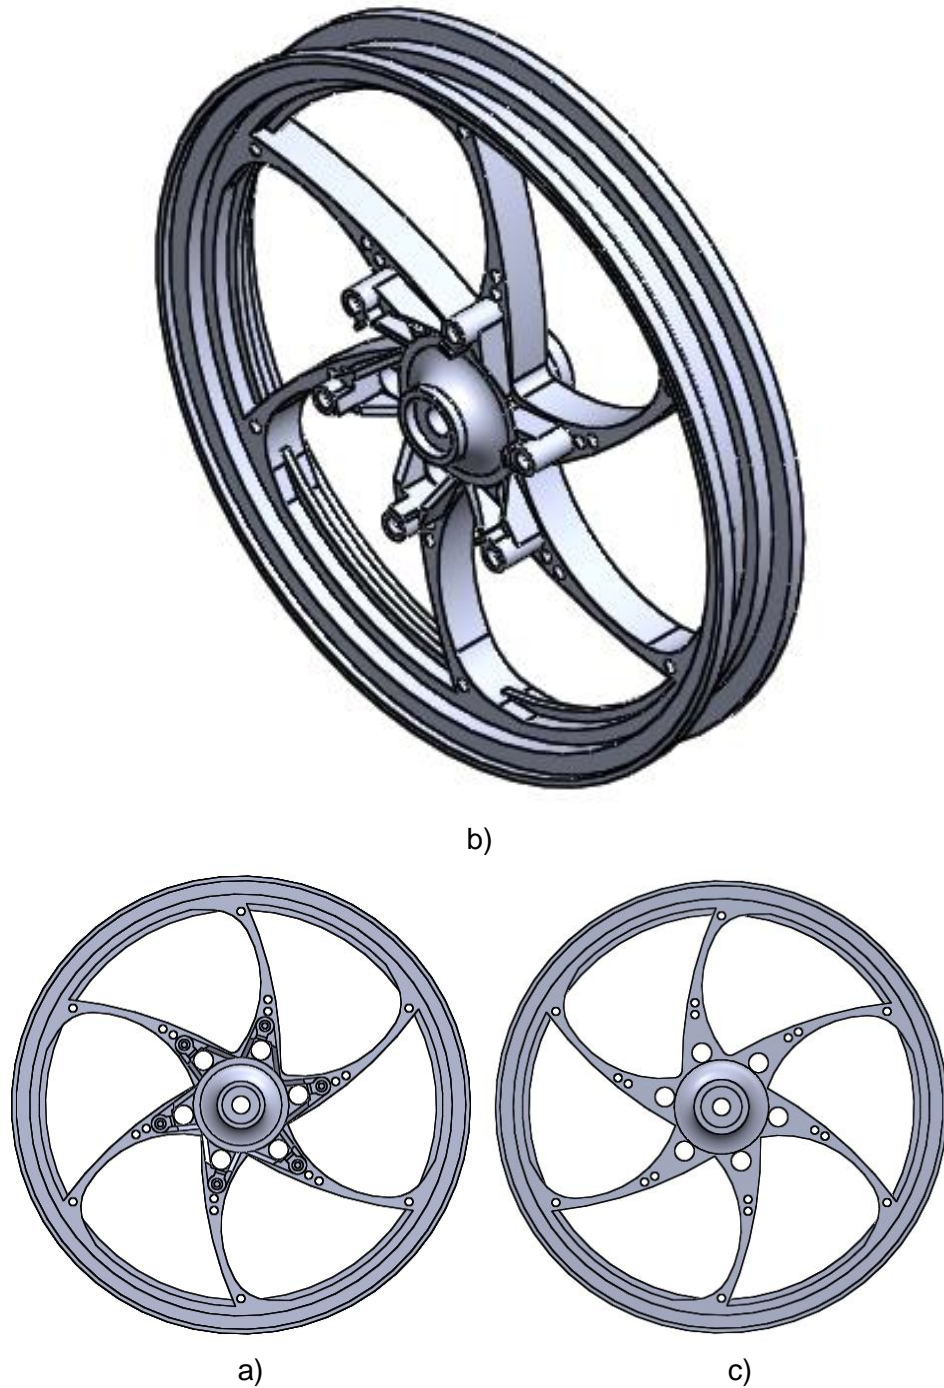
Diseño optimizado “a.4” a) Vista frontal. b) Vista isométrica. c) Vista trasera.
